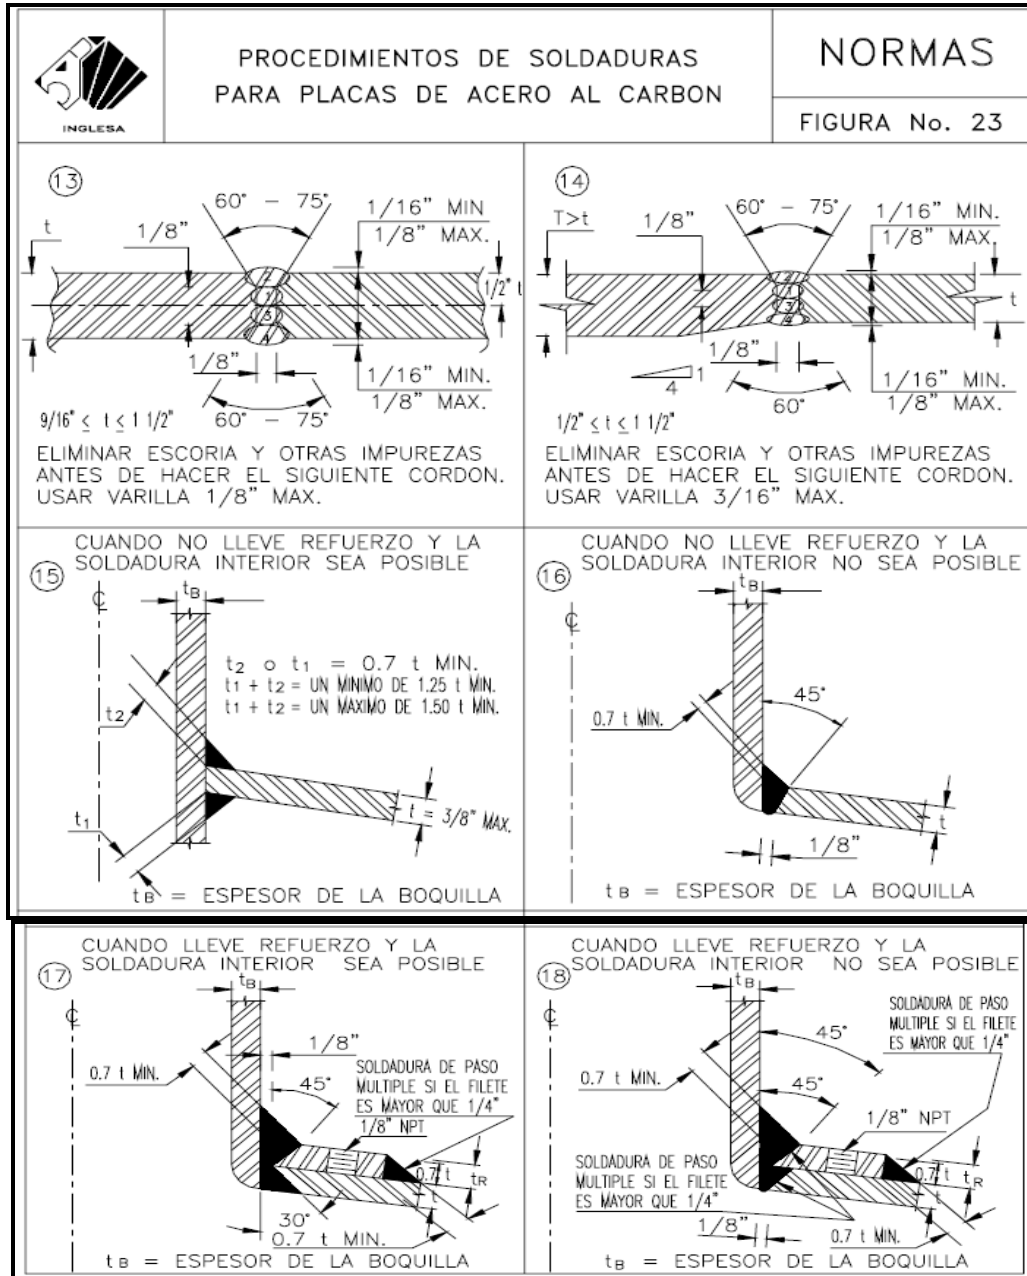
10. Tipos de soldadura para placas de acero al carbono<sup>170</sup>. Fuente:
